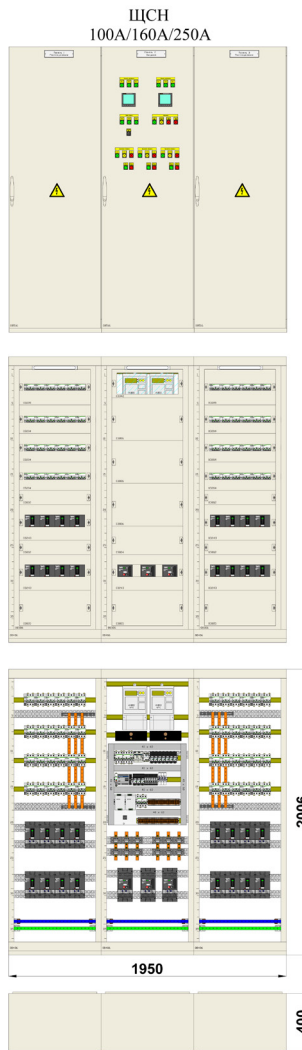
Габаритный чертеж ЩСН на ток 100-250А
